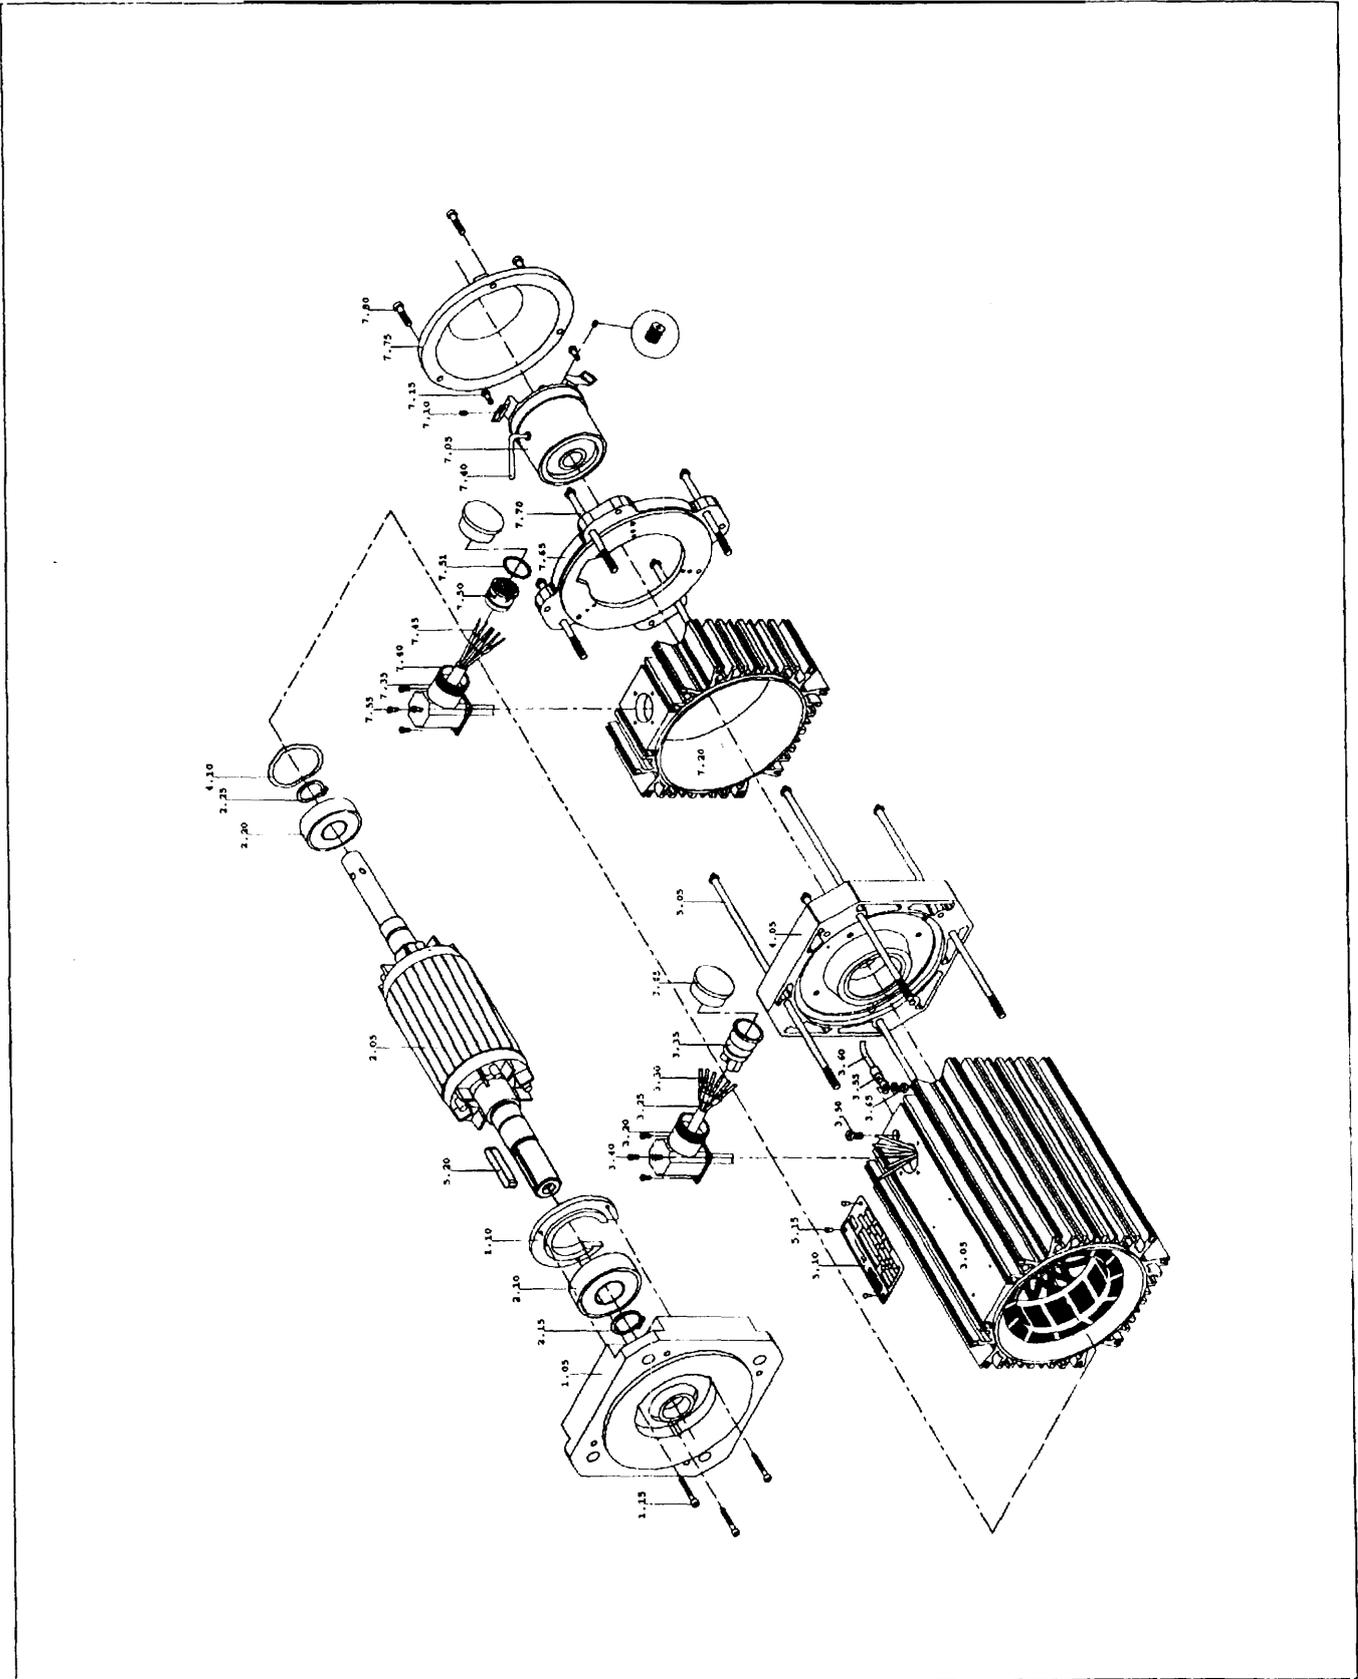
Explosionszeichnung Motor mit Bremse ohne Lüfter DSVABS
